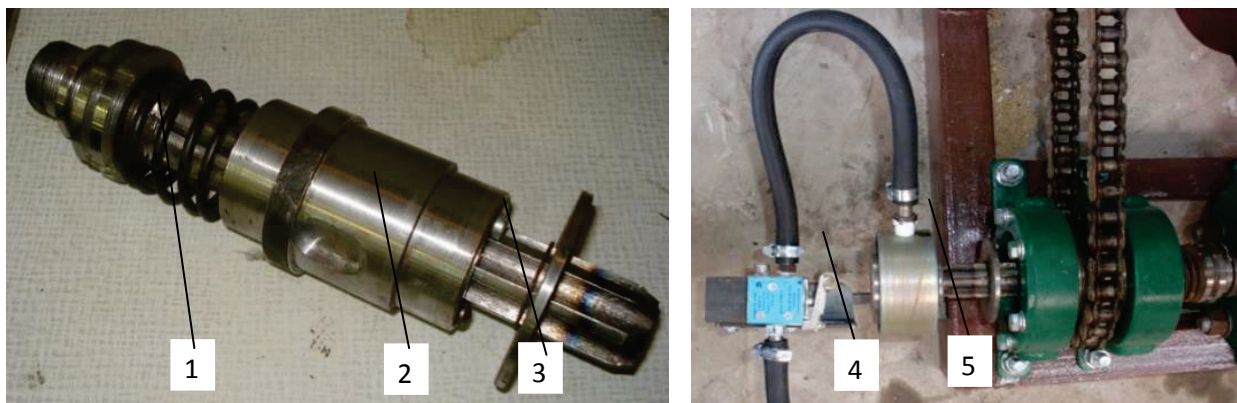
Механізм увімкнення пневморозподільника, та його з'єднання з вмикачем трилінійного типу П-РКЗ.4: 1 – пружина; 2 – корпус; 3 – шліцьовий вал знапівкруглими канавками; 4 – пневморозподільник; 5 - пневмоперехід
